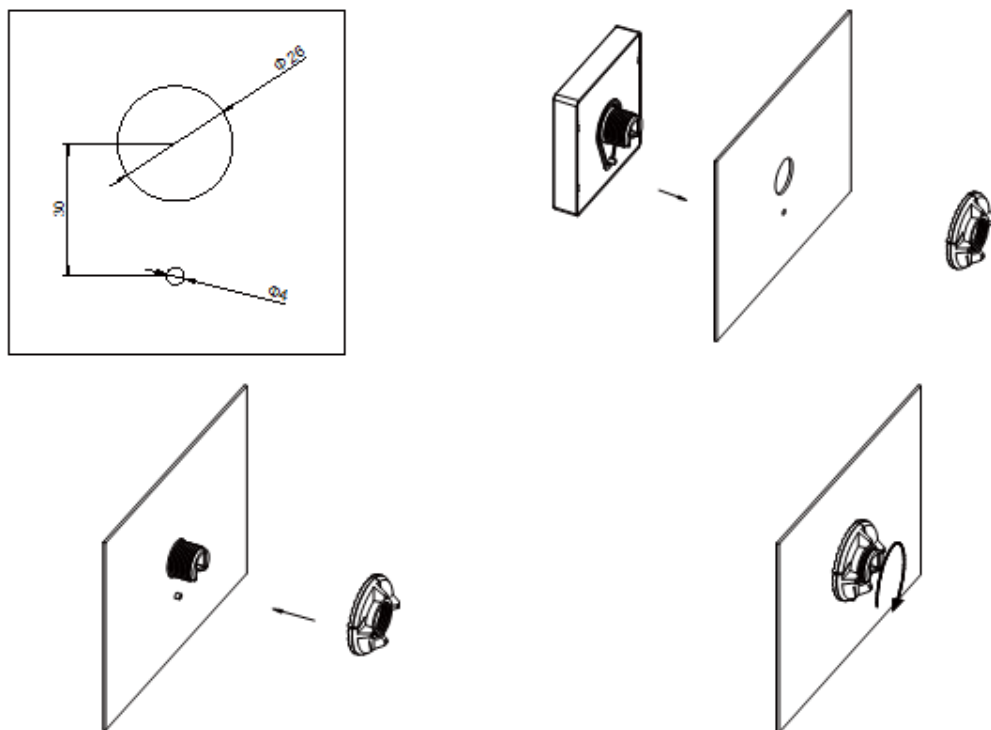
Установка модуля дисплея D1. Способ установки
